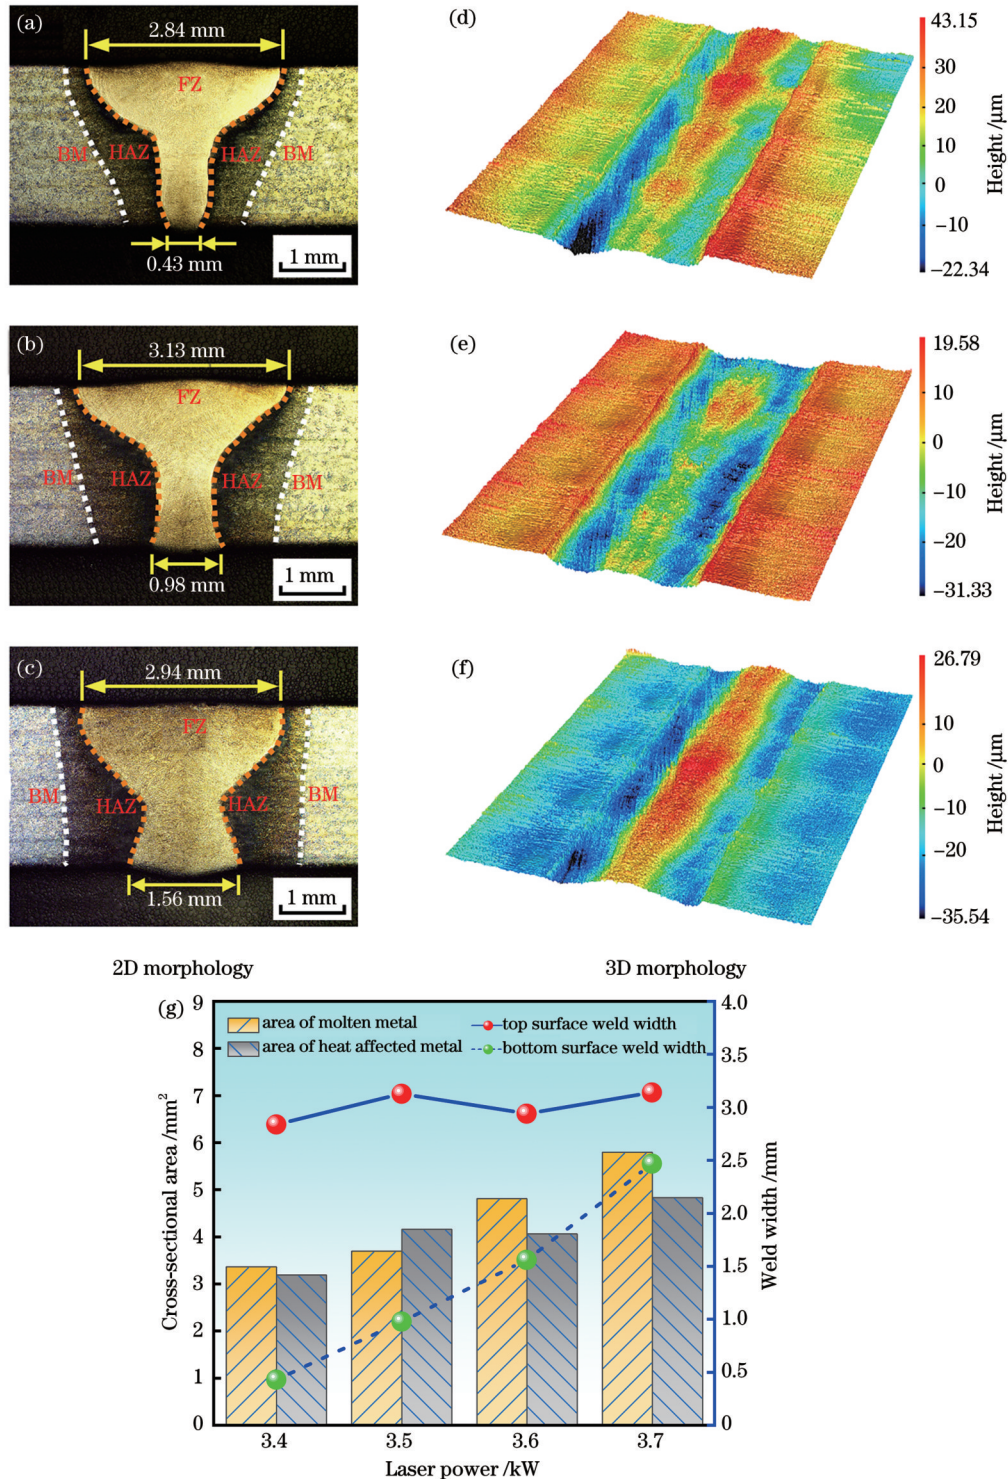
不同激光功率下焊接接头的横截面形貌及尺寸。(a)(d)3.4 kW, 形貌;(b)(e)3.5 kW, 形貌;(c)(f)3.6 kW, 形貌;(g)尺寸
